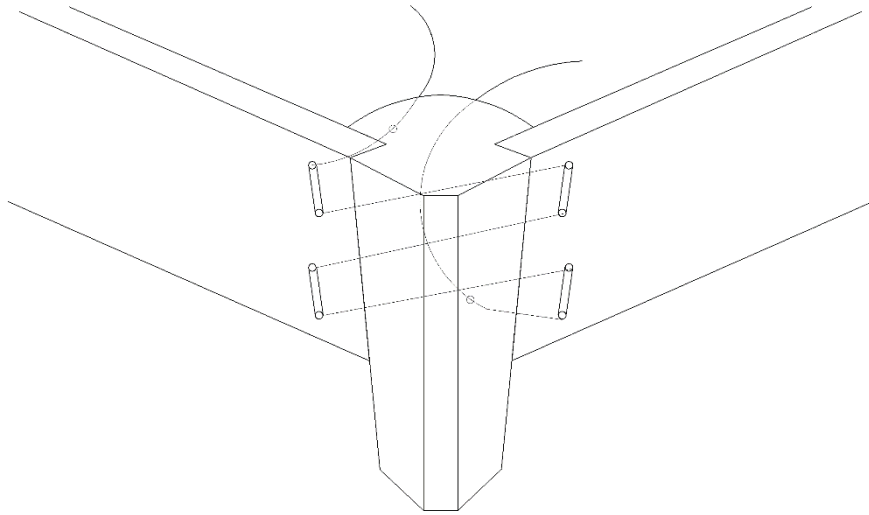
Схема сопряжения и прошивки бортовых досок при креплении к штевню. Переход обшивки «клинкер» в обшивку «вгладь»
